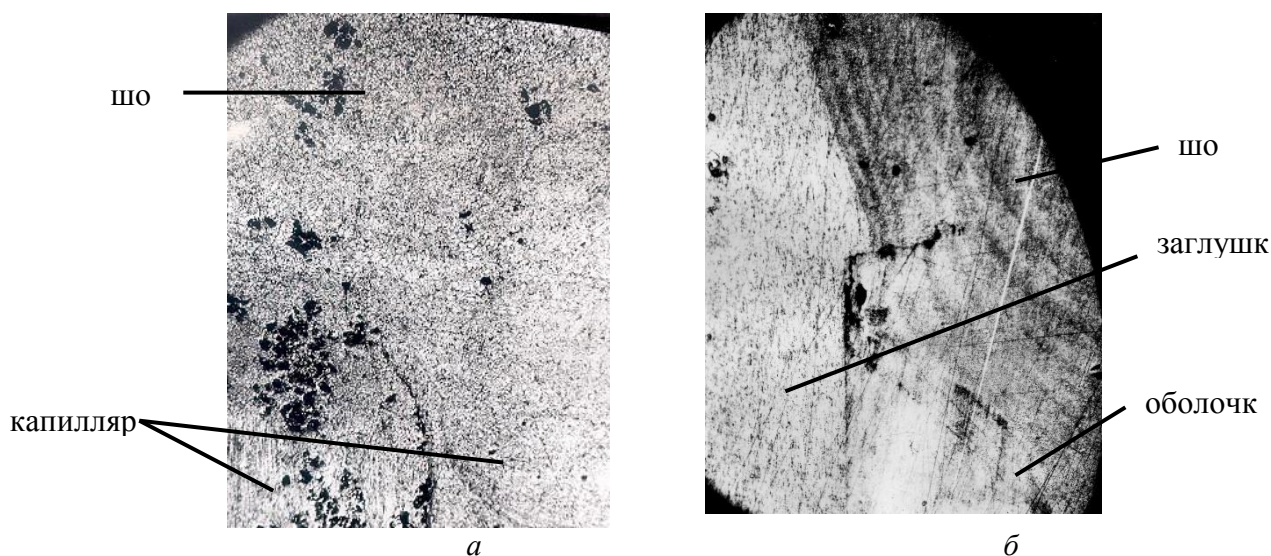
Сварные соединения, выполненные дуговой сваркой методом оплавлением торца (а - х70) и дуговой сваркой в импульсном режиме стыкозамкового шва (б - х70)
